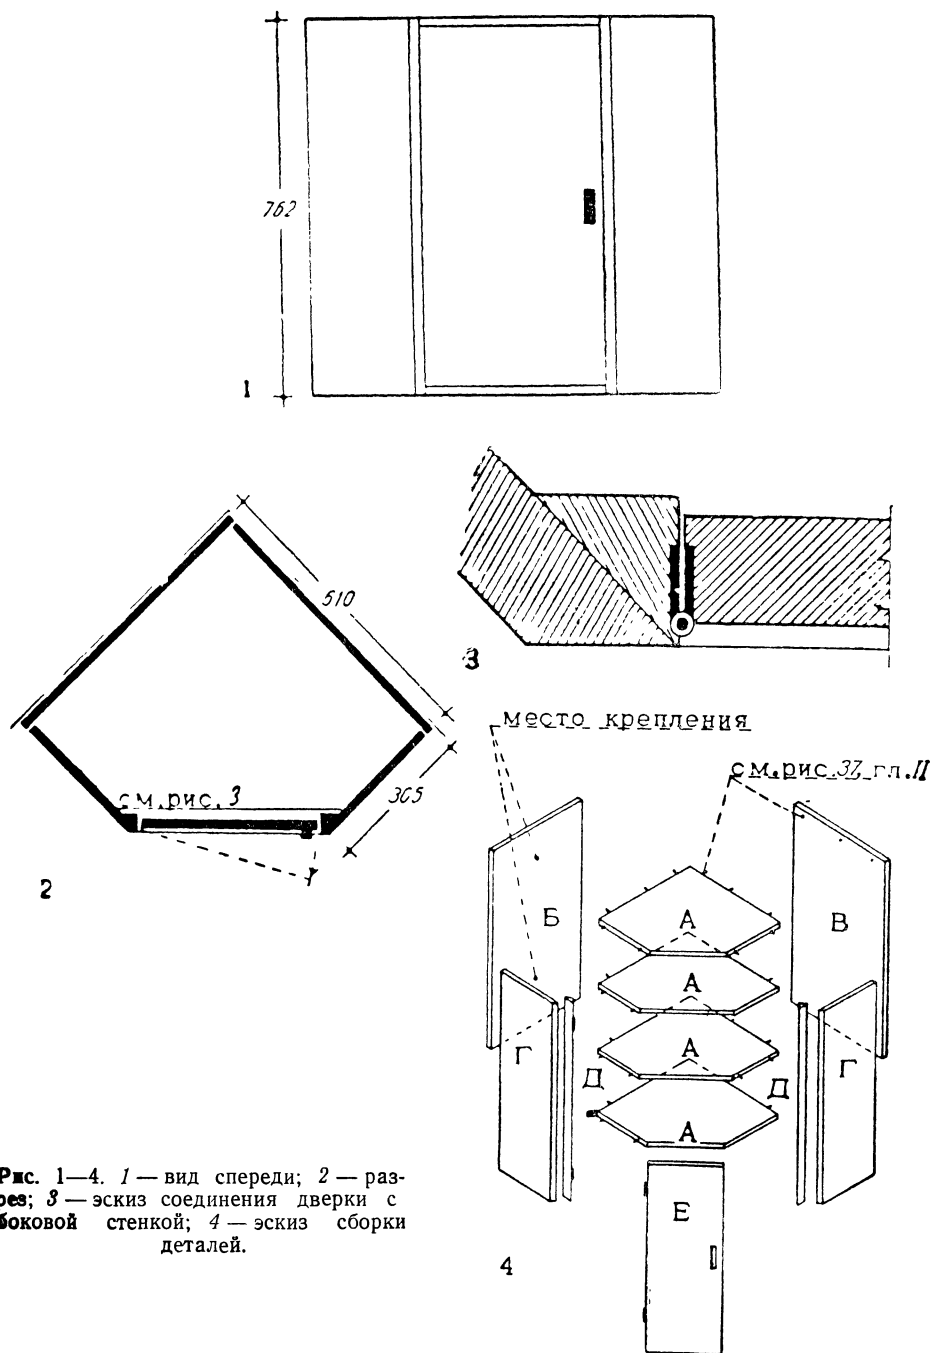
4. 1 — вид спереди; 2 — разрез; 3 — эскиз соединения дверки с боковой стенкой; 4 — эскиз сборки деталей.
